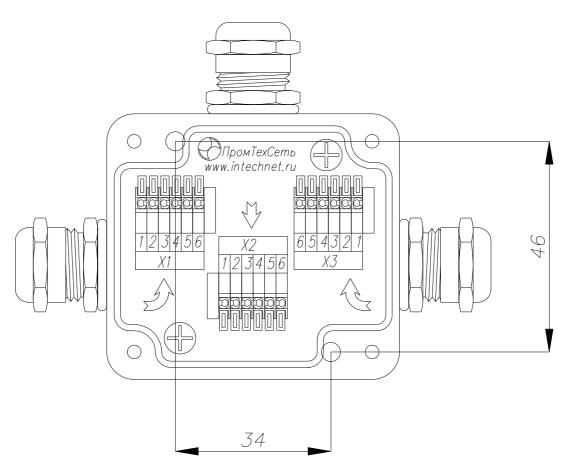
Компоновка и разметка места установки разветвителя РПМ-3
